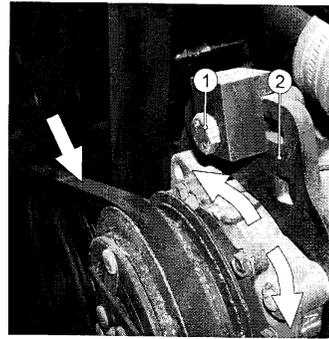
Проверка натяжения ремня привода компрессора кондиционера:
